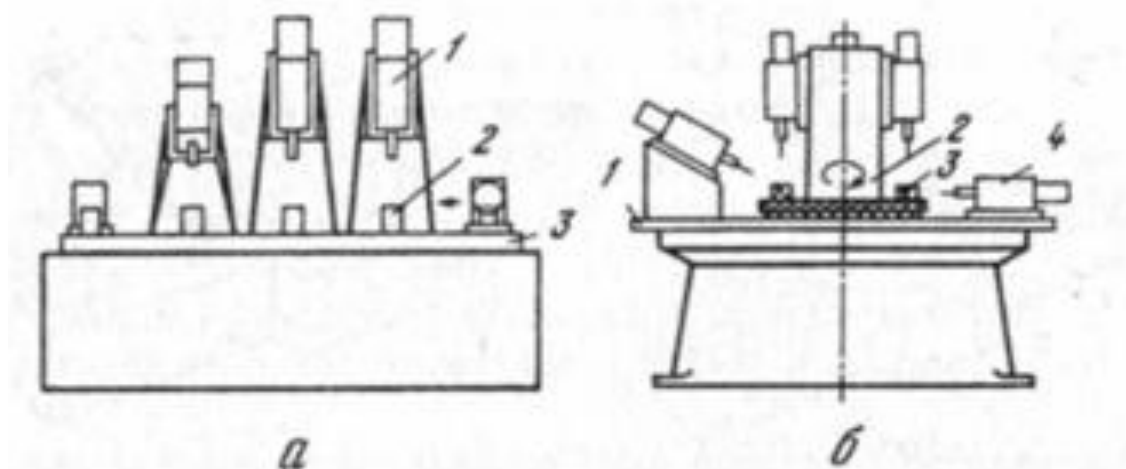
Компоновка агрегатных станков: а - с прямолинейным перемещением заготовок, б – с центральной колонной.
